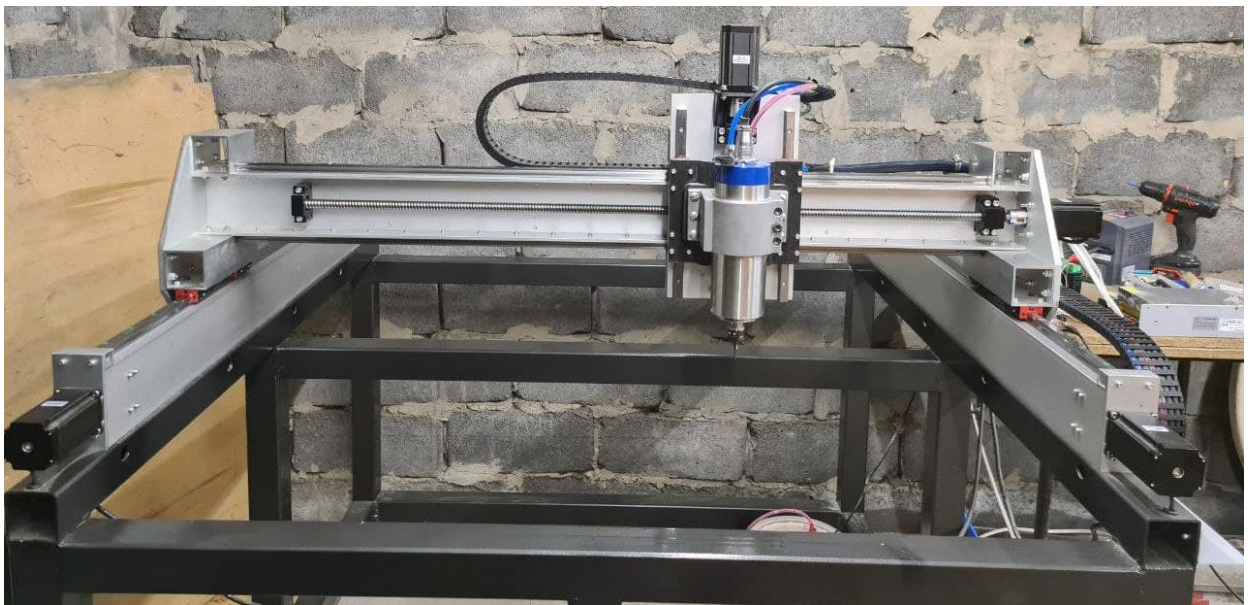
Зібраний макет фрезерного верстату з ЧПК, вид спереду
